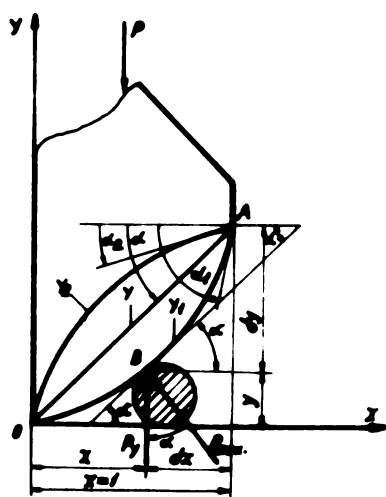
Geometria tăișului cuțitului în plan longitudinal
